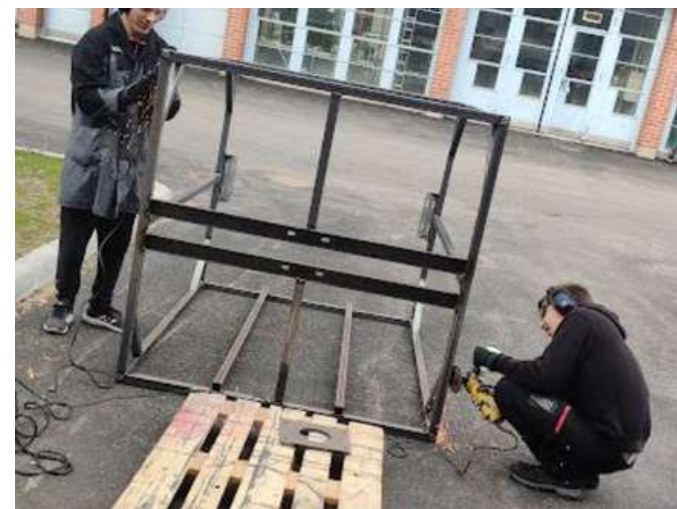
Pulido de material sobrante de soldaduras. Fuente: Elaboración propia.
